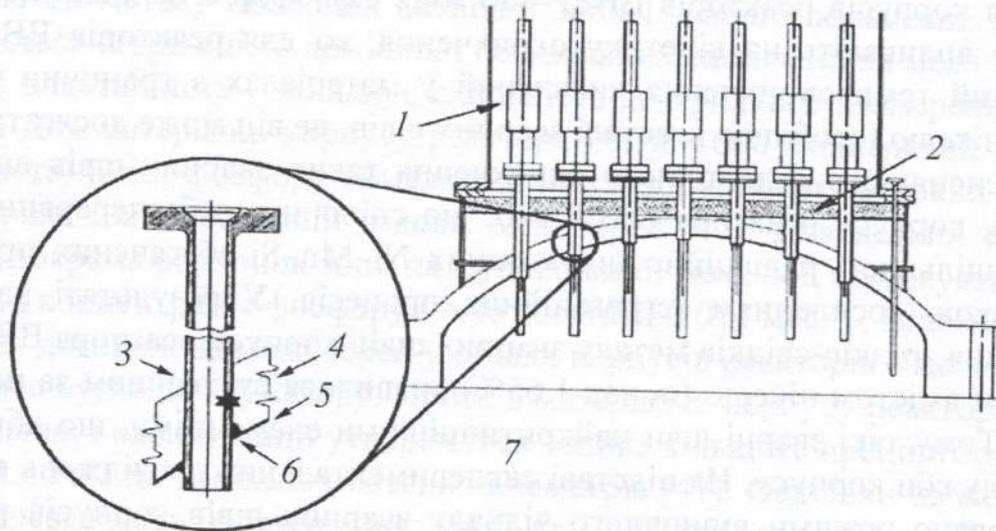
Поперечний переріз кришки реактора з вертикальними металевими трубками для приводу СУЗ. Зірочка вказує місце виявленої тріщини і витоку теплоносія на АЕС Osconee [37]:
